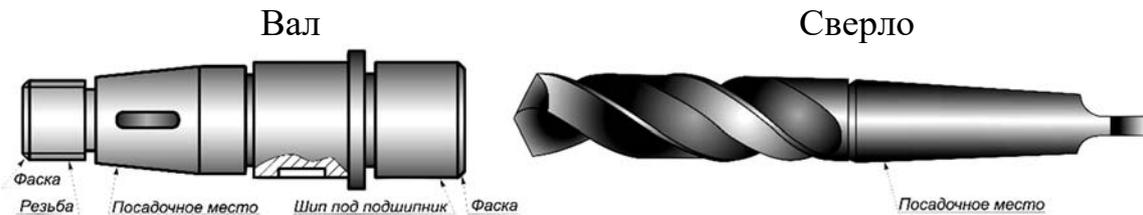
Примеры деталей с коническими поверхностями
